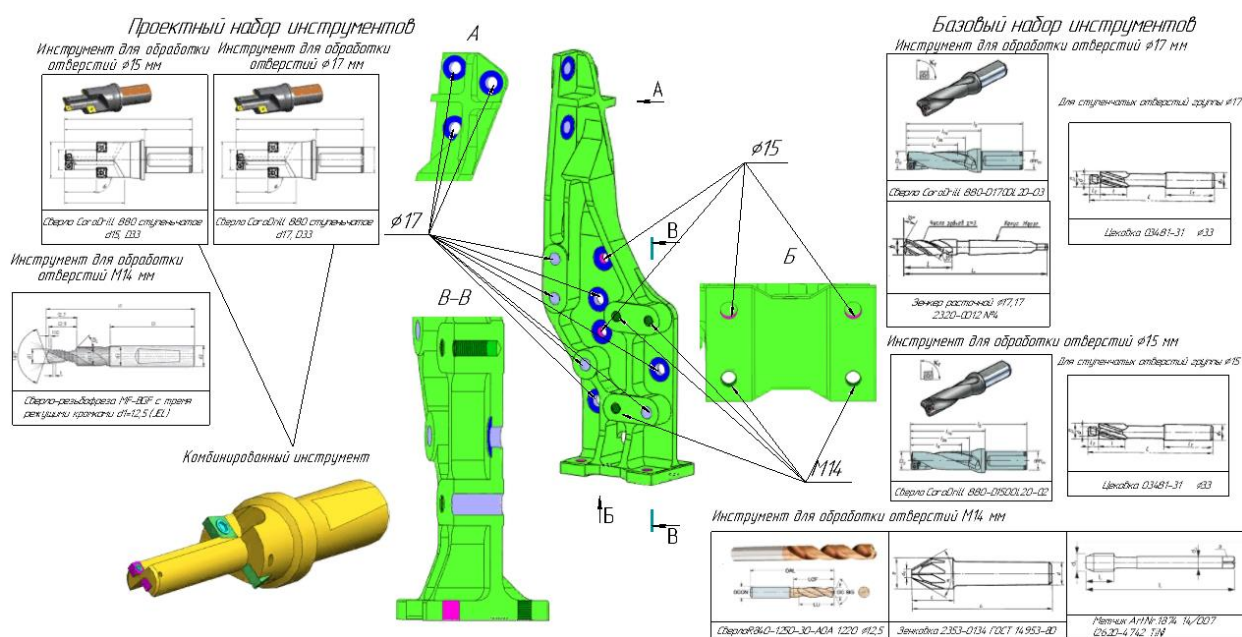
Обработка отверстий в детали «Кронштейн»
